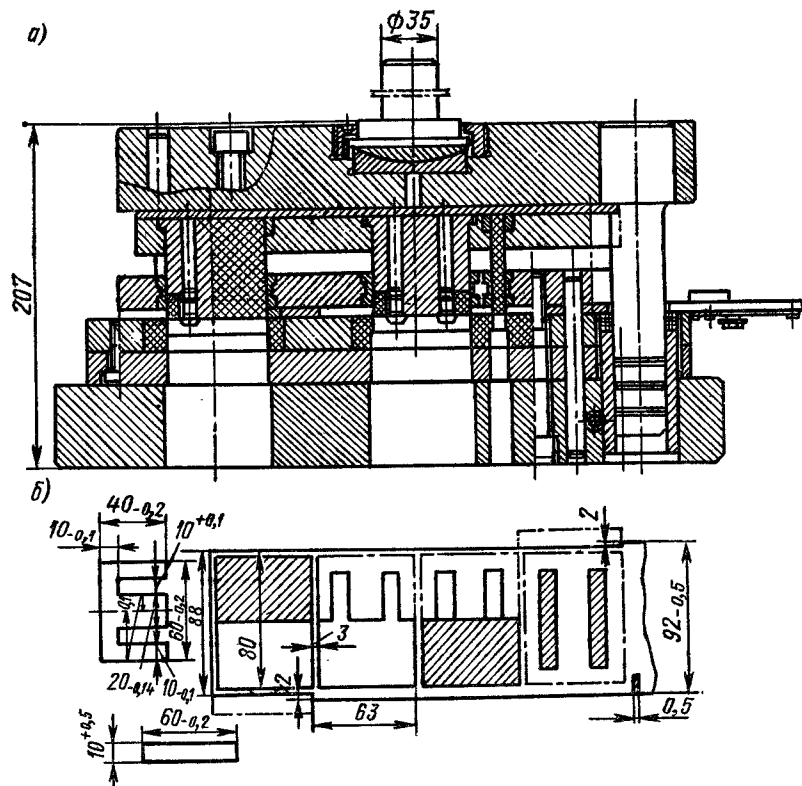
Последовательный штамп с твердосплавными вставками (а) для пластин трансформатора (б)
